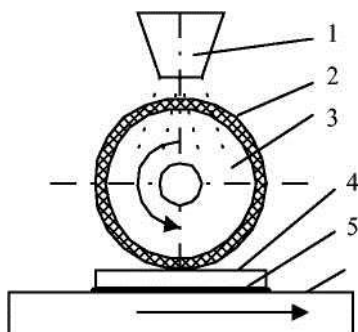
Схема різки диском із зовнішньою алмазосодержащою ріжучою кромкою: 1 - сопло подачі смазуюче-охолоджуючої рідини; 2 - ріжуча кромка диска; 3 — основа диска; 4 — розрізаюча пластина; 5 - клеювальний матеріал; 6 - облямовування для закріплення пластини
